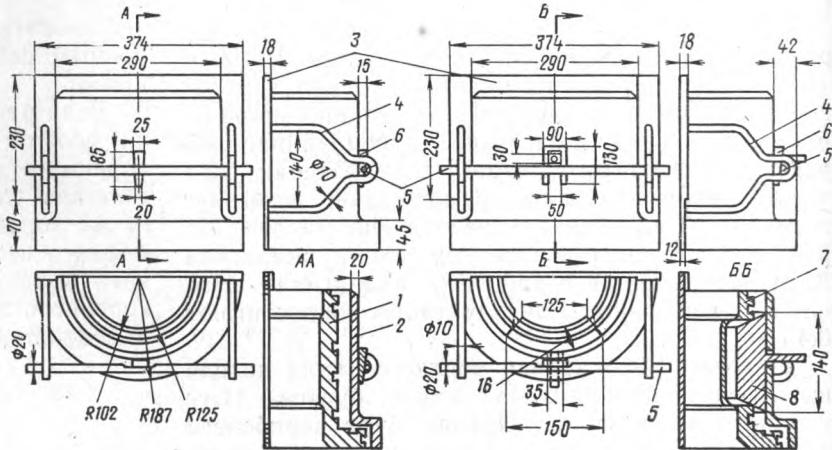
Вкладыши моторно-осевого подшипника тягового электродвигателя в форме для заливки:
